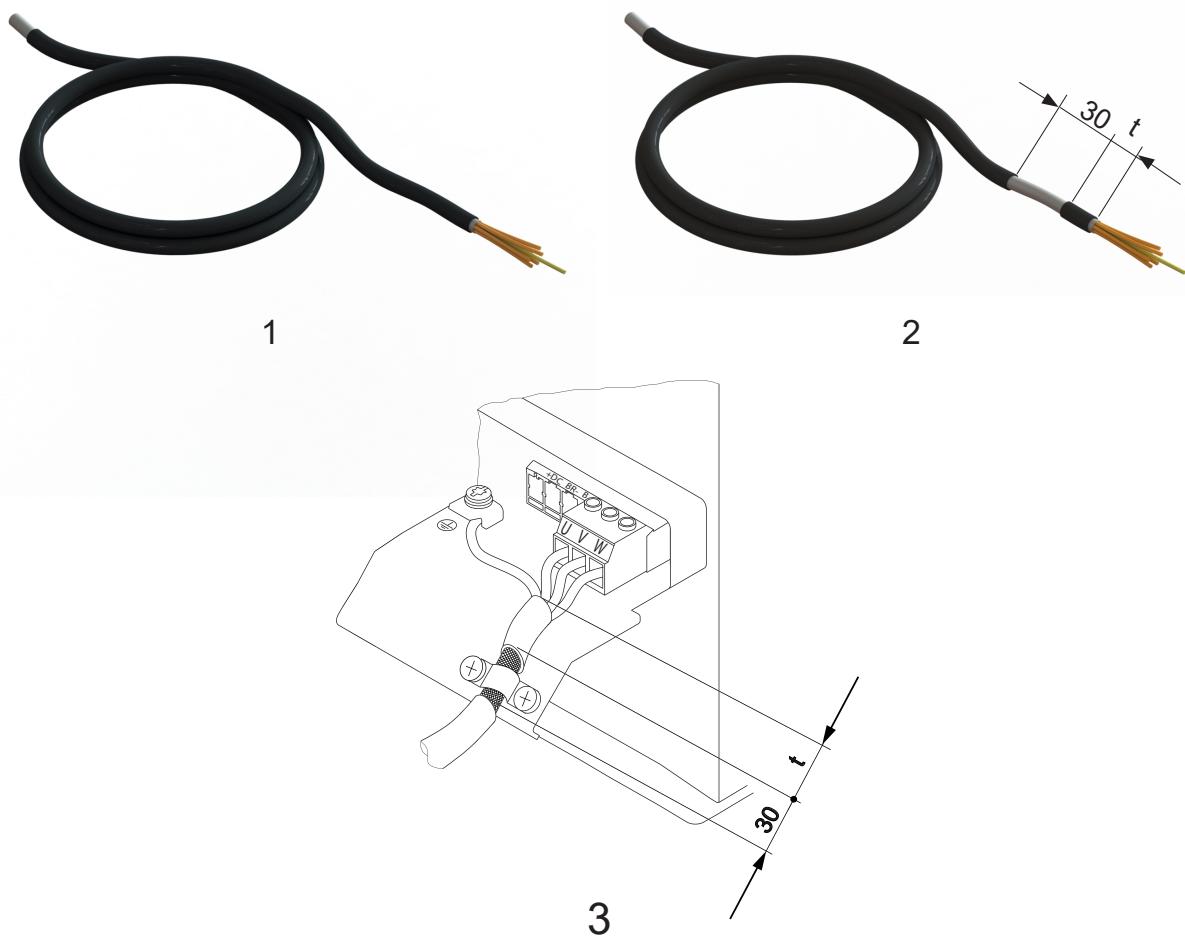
Kabel pro připojení motoru s integrovanými řídícími vodiči
